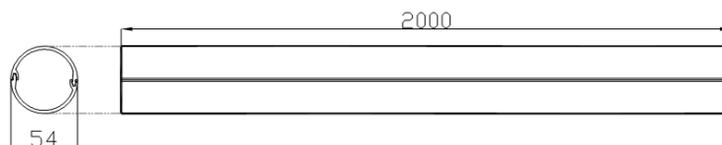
Dimensiones Protector de Cable Pre ensamblado
